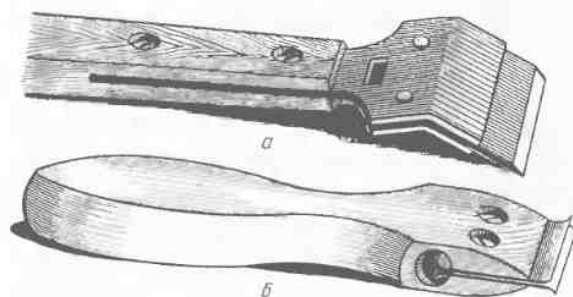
Стандартные цикли: а — для циклевки полов с длинной ручкой и набором сменных лезвий; б — двусторонняя цикля с двумя загнутыми лезвиями
